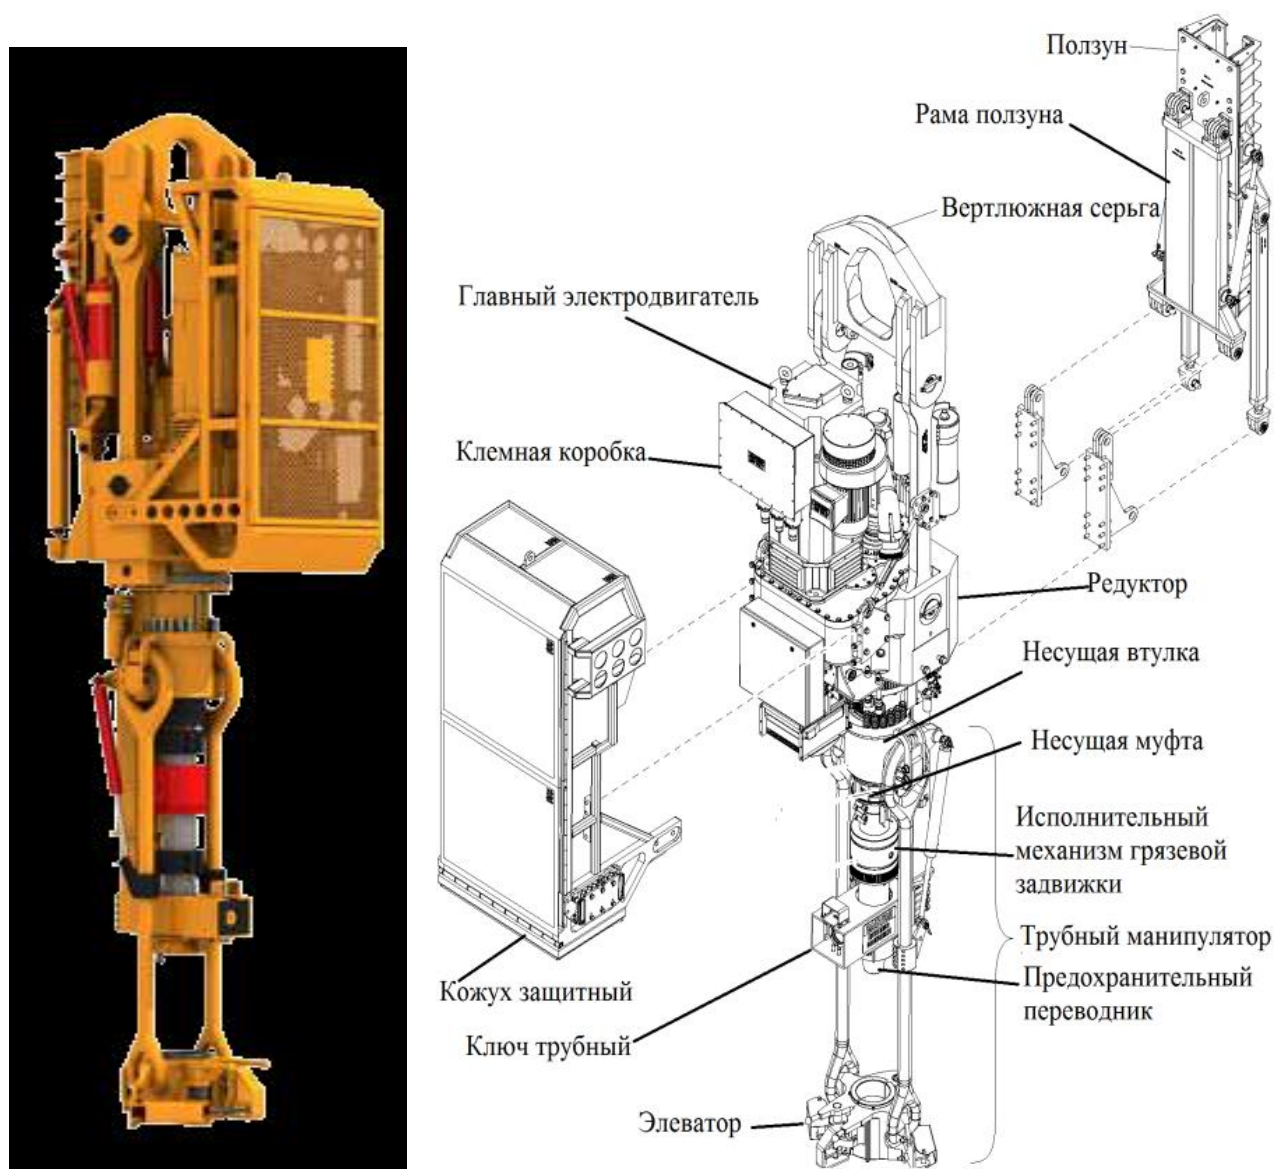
Внешний вид исполнительного модуля и элементы конструкции
